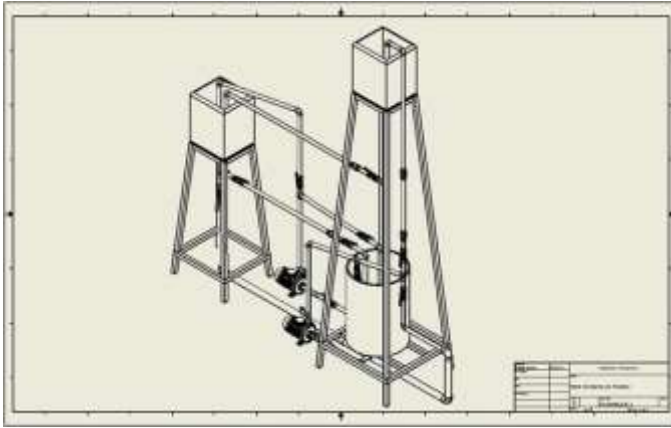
Plano isométrico del Banco de pruebas propuesto.
